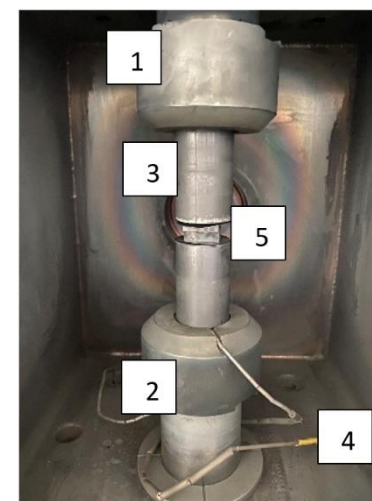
схема размещения заготовок перед электрической сваркой сопротивлением: 1 – гидравлический цилиндр, 2 – графитовая вставка, 3 – пуансоны, 4 – термопара, 5 – свариваемые заготовки.
